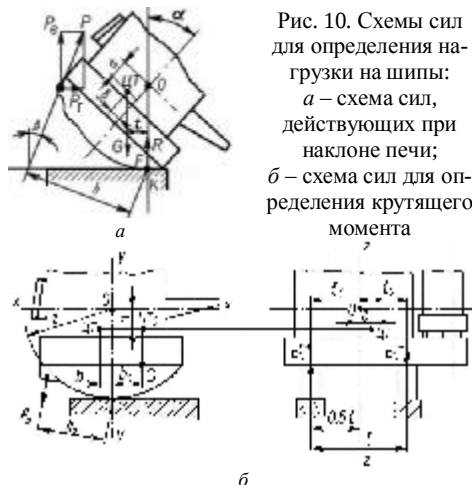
Схемы сил для определения нагрузки на шипы: а – схема сил, действующих при наклоне печи; б – схема сил для определения крутящего момента
